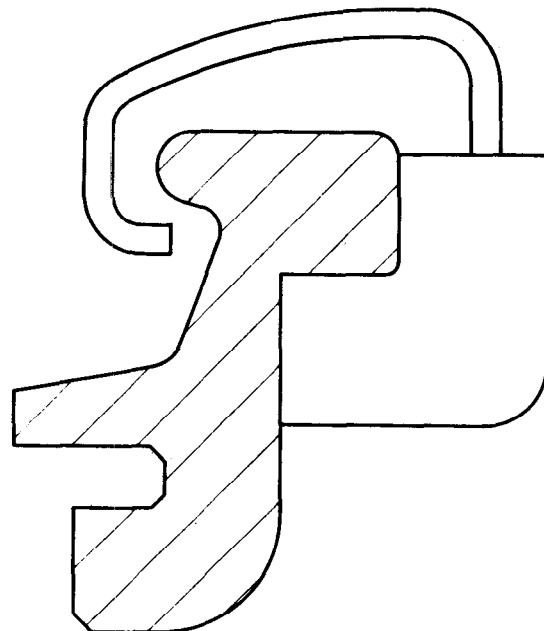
C-förmiger Flanschring aus Sinterstahl mit kombiniertem Nylon-Stahl-Läufer
